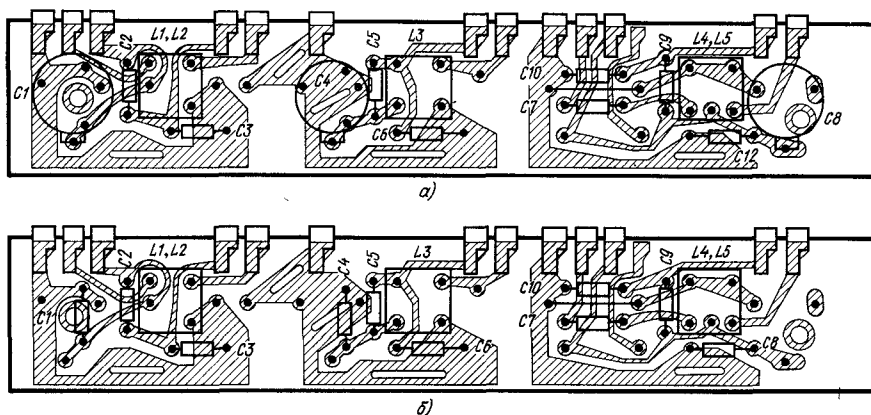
Электромонтажная схема печатных плат блока KB (A2) РПУ: а — планок KB 52—75 м; б — планок KB 49, 41, 31 и 25 м
